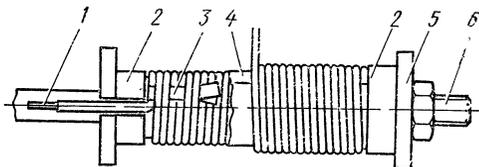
Намотка двухслойной цилиндрической обмотки НН трансформатора типа НОМ-35-66:
